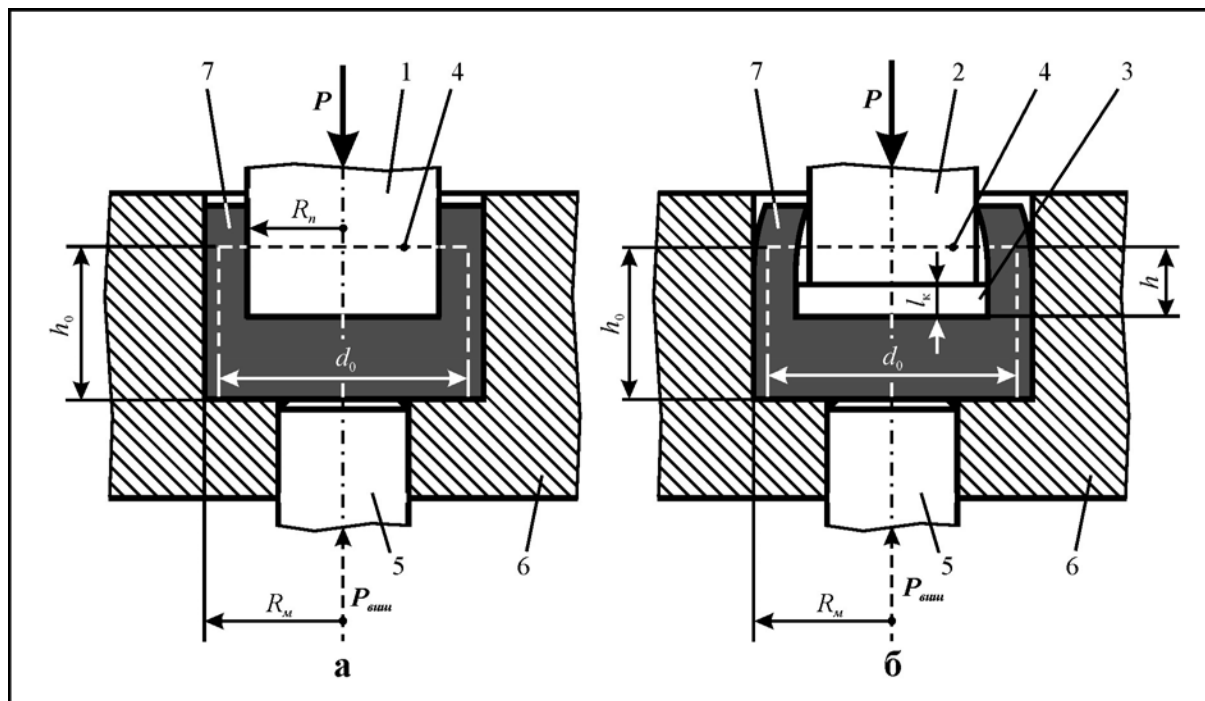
Схеми процесу зворотного видавлювання: а – циліндричним пуансоном 1; б – пуансоном 2 з пояском, що калібрує; 4 – заготовка; 5 – виштовхувач; 6 – матриця; 7 - виріб
